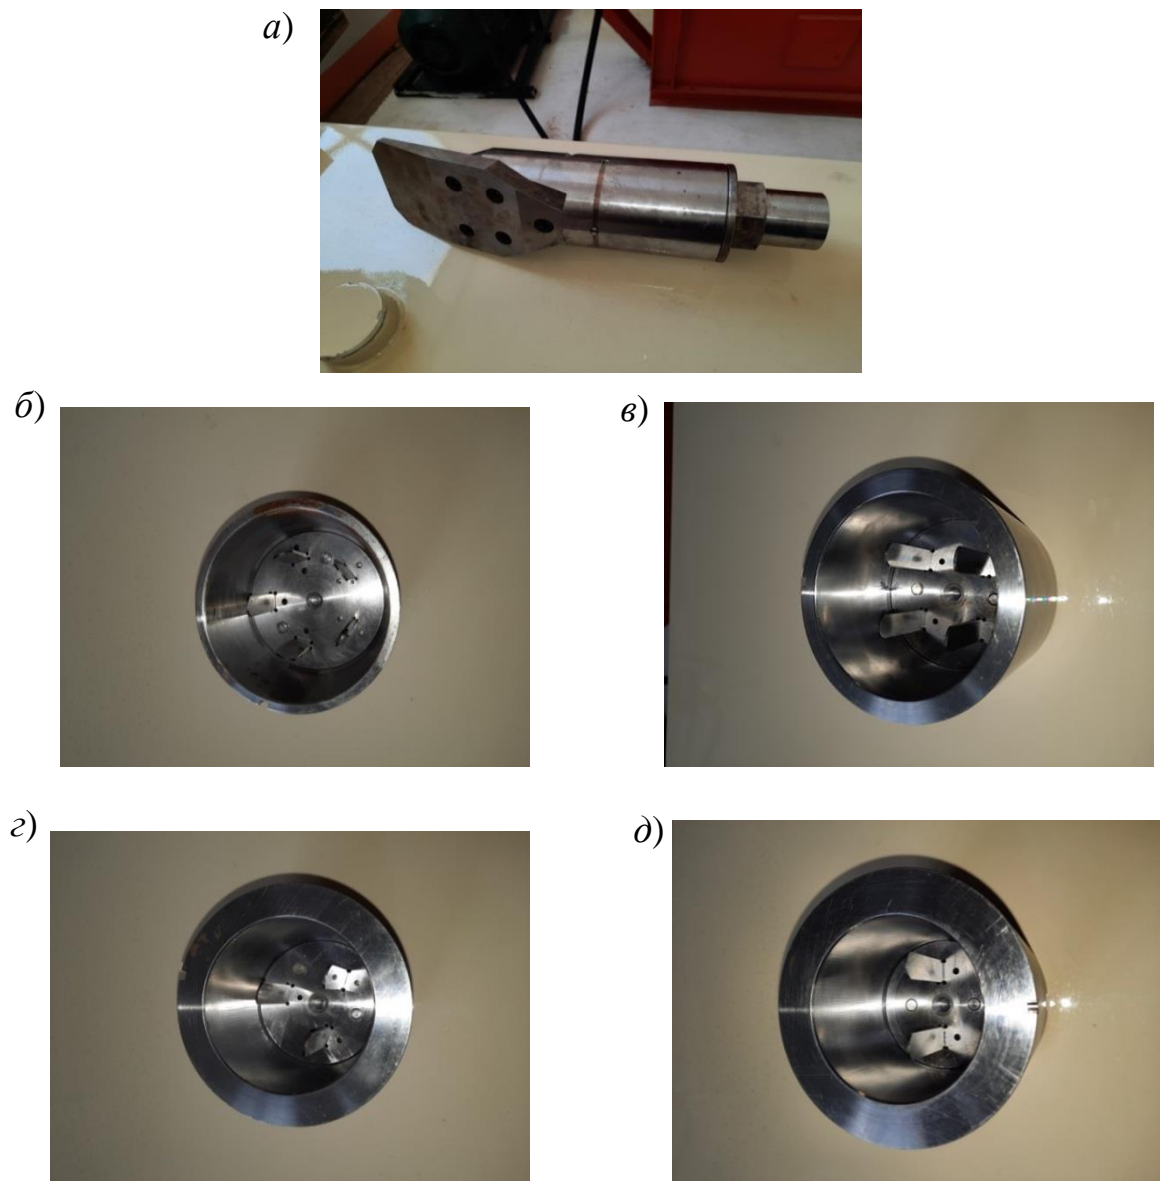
Опытный образец рабочей головки ВГВК: *a* – в сборе;
